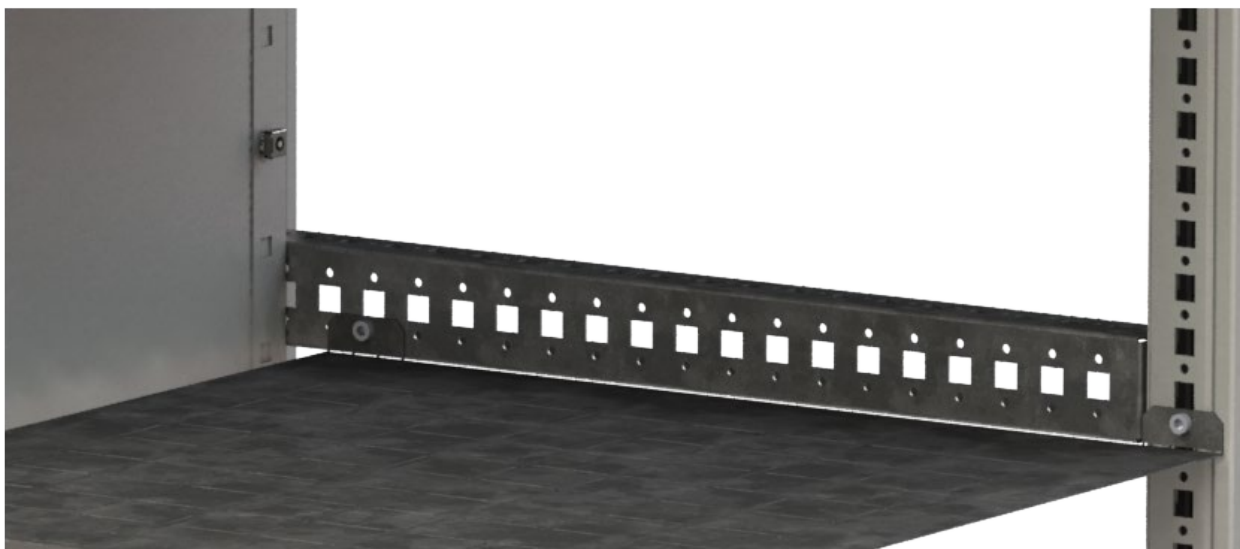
Вариант установки горизонтальной перегородки с пластронами.
